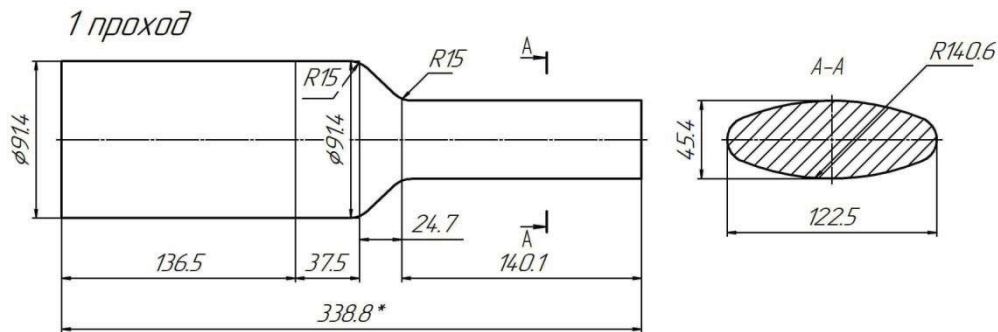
Эскиз заготовки после первого прохода вальцовки по схеме круг-овал
